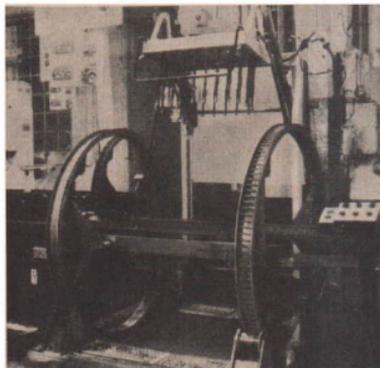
/1 Rhönrad und 22-Spindelschrauber für Ölwannenschrauben
